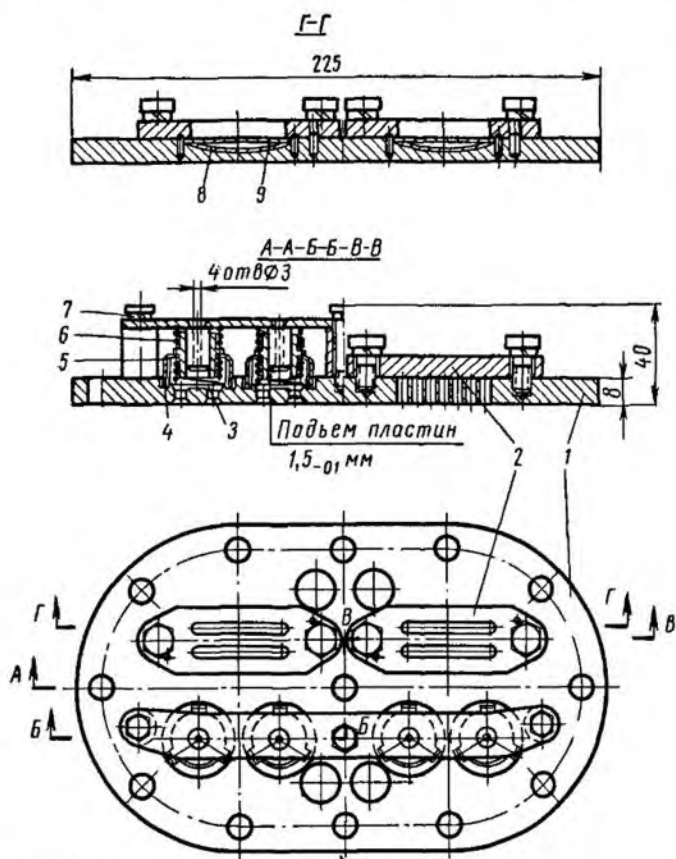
Клапанная плита компрессора ФВ-4 со всасывающими полосовыми и нагнетательными пяточковыми клапанами:
